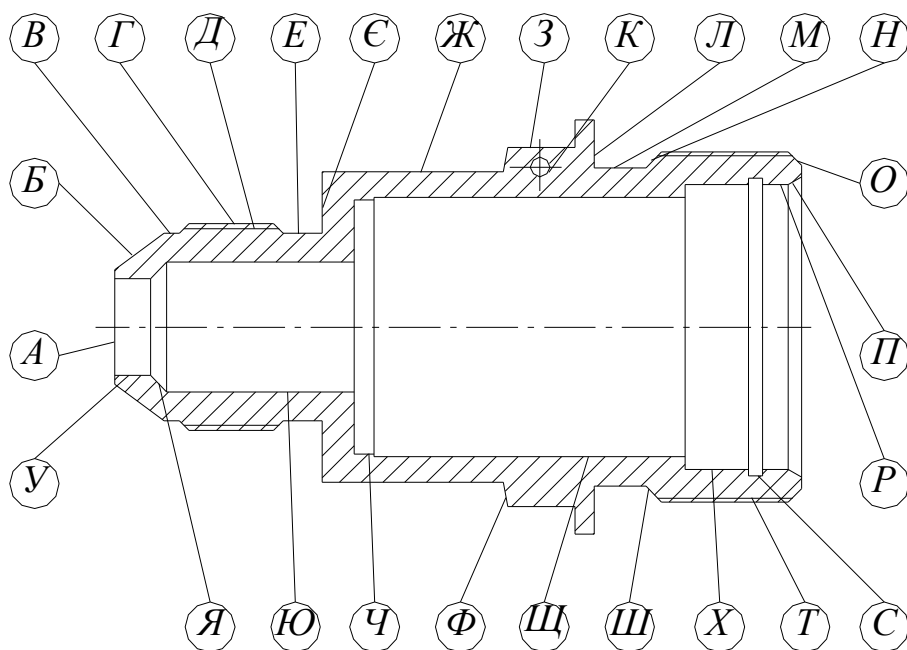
Позначення поверхонь деталі Корпус 027076081
